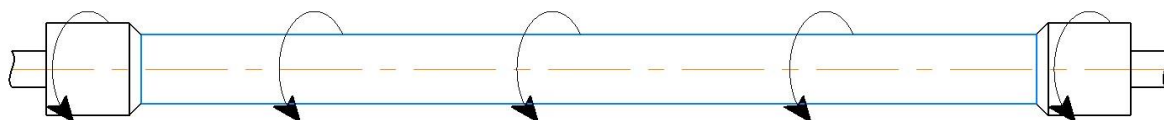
Схема вращения трубной заготовки при работе установки ТВЧ
